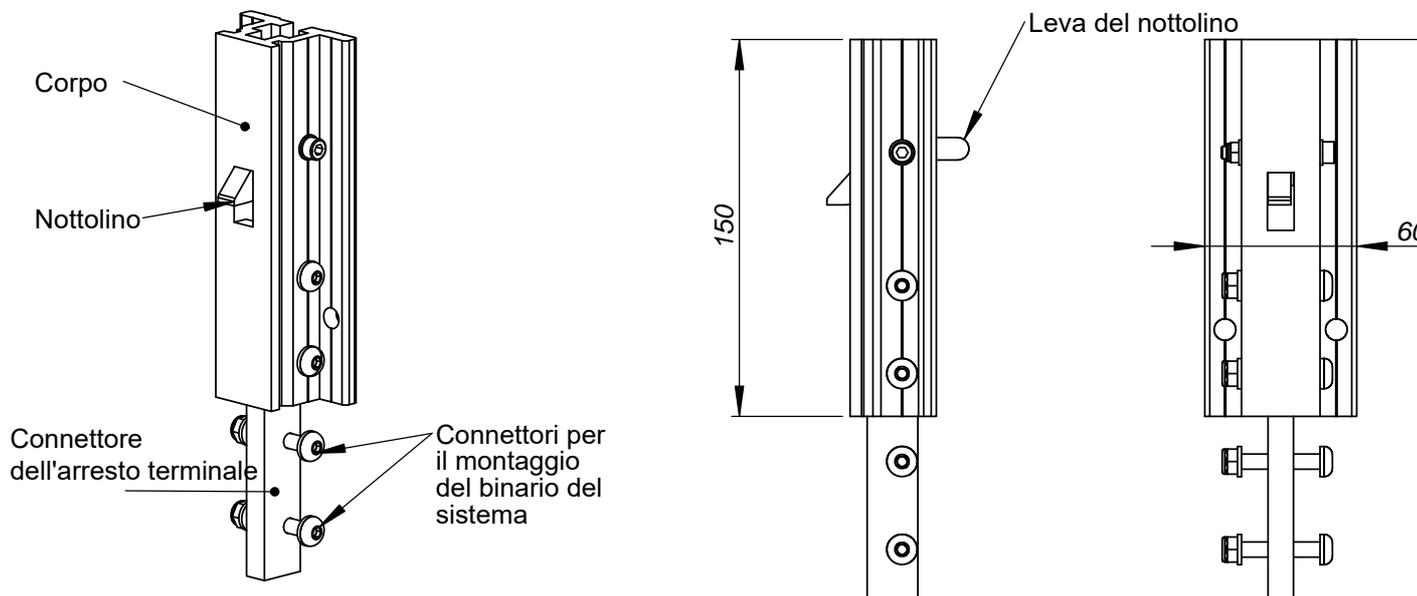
AC520-210 Arresto terminale superiore (struttura, componenti, dimensioni base).
